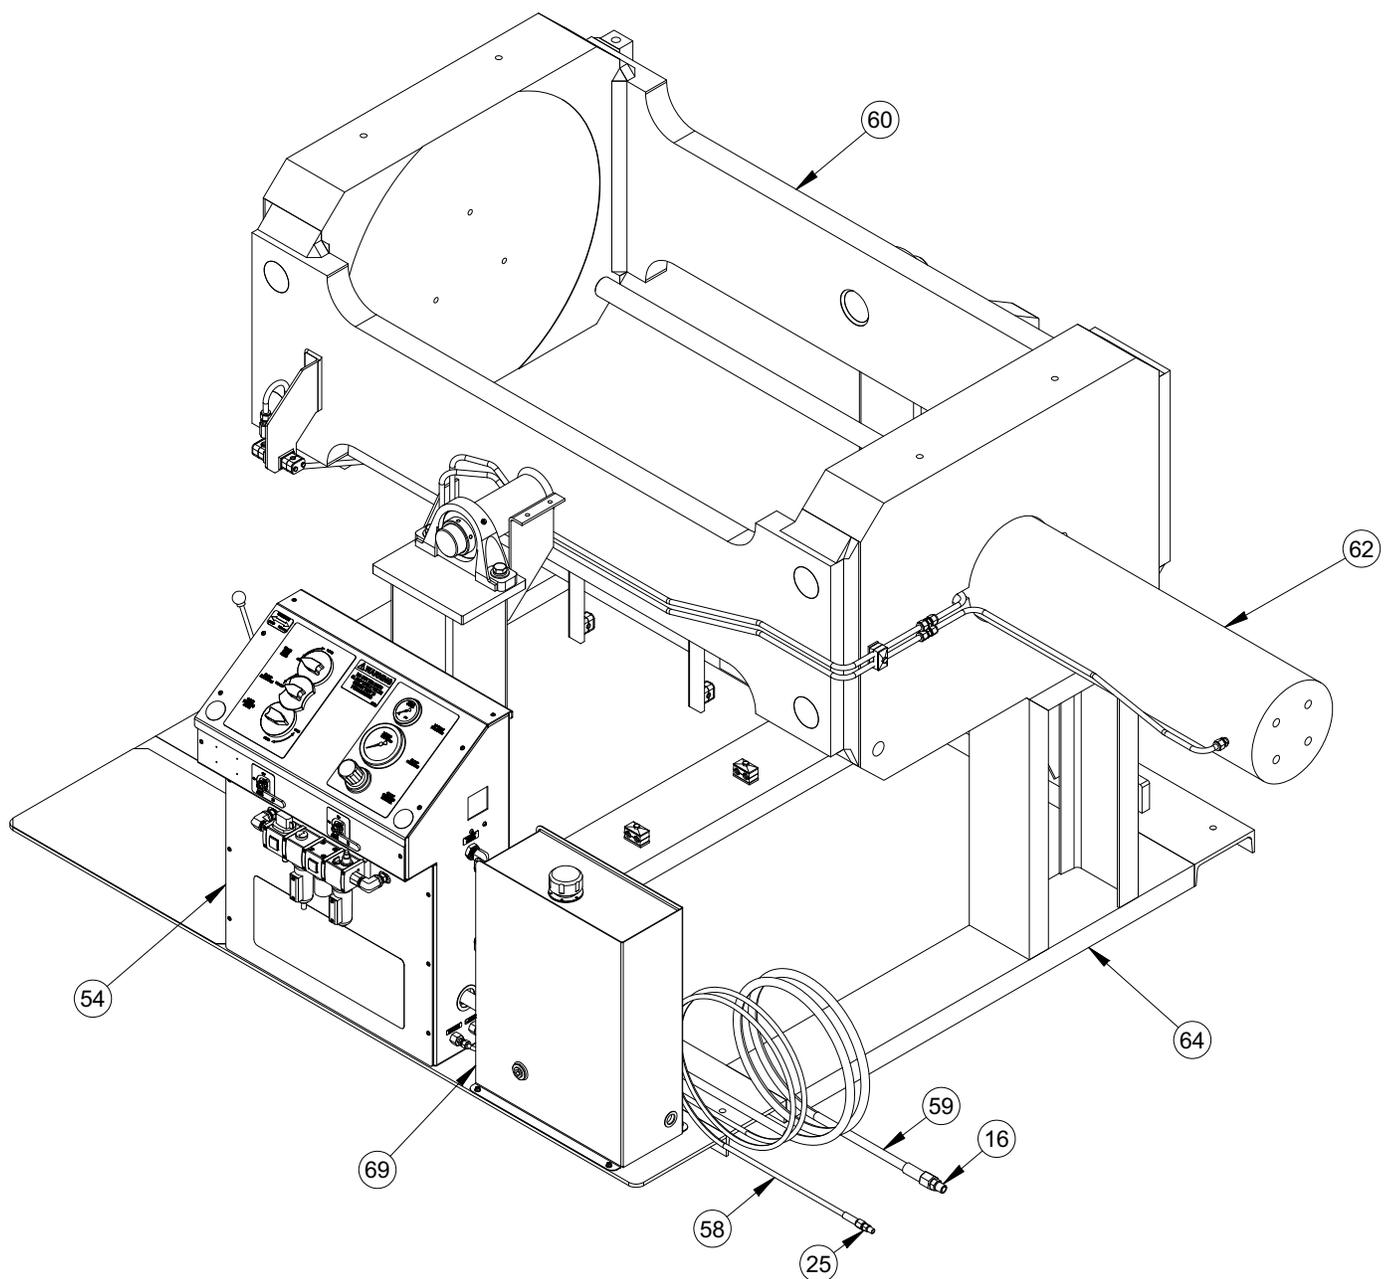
USV-24-300T ENSEMBLE 1 (P/N 89889)
